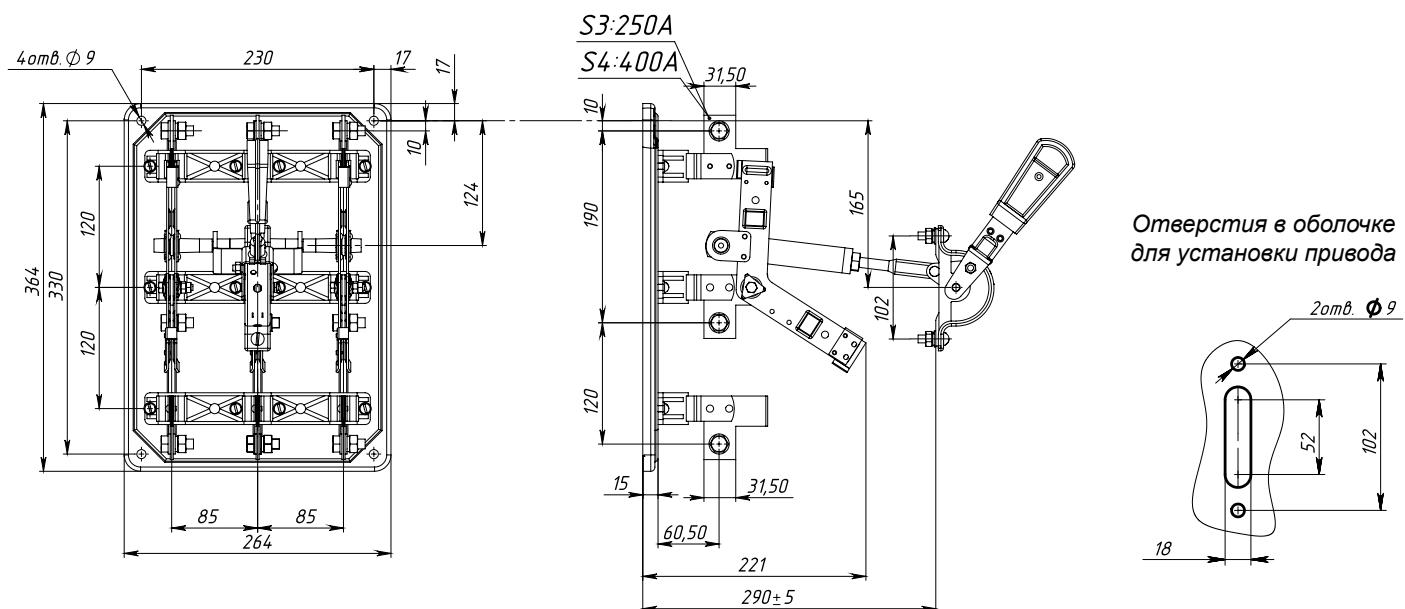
Разъединитель типа ПЦ с центральным приводом на токи 250 А и 400 А
